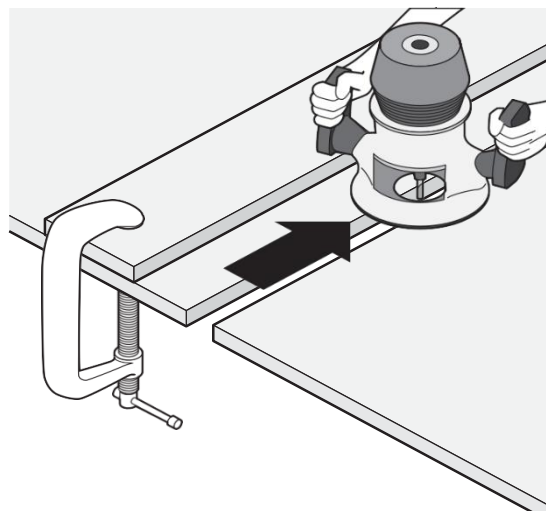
Фрезерная подгонка торцов (Зеркальная обработка фрезером)
